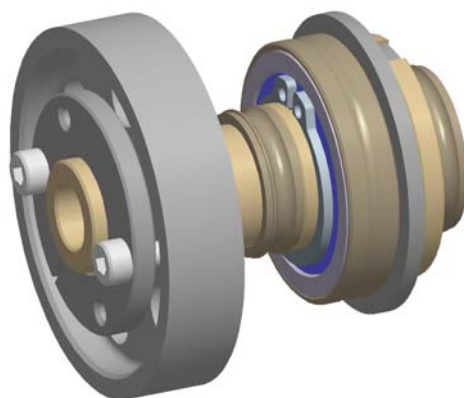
Model en CAD del conjunt de peces que formen l'arbre d'entrada
